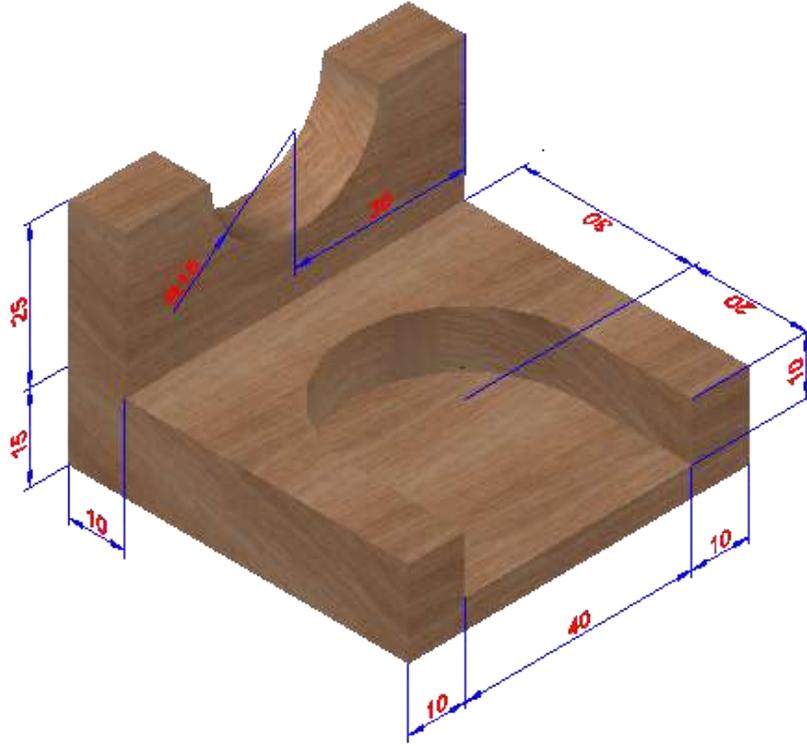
ارسم مسقطا وافيا للمسند الجانبي
